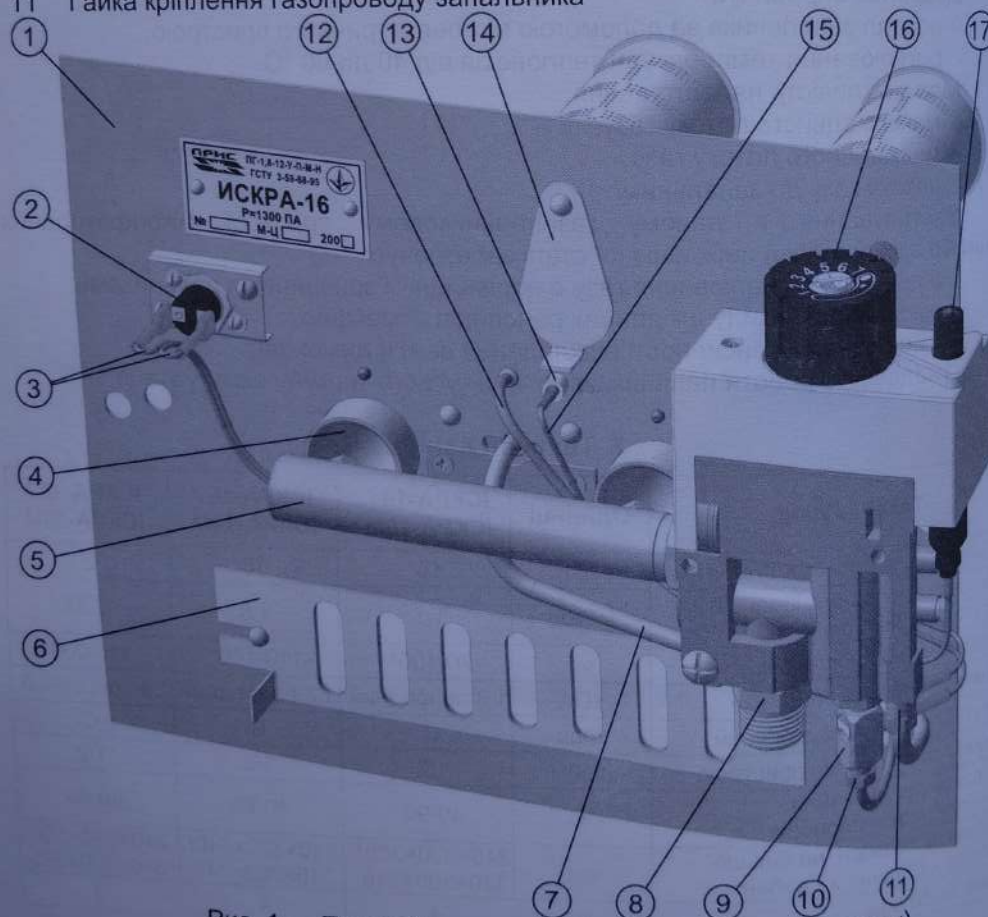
Пристрій газопальниковий ИСКРА (вид спереду)
